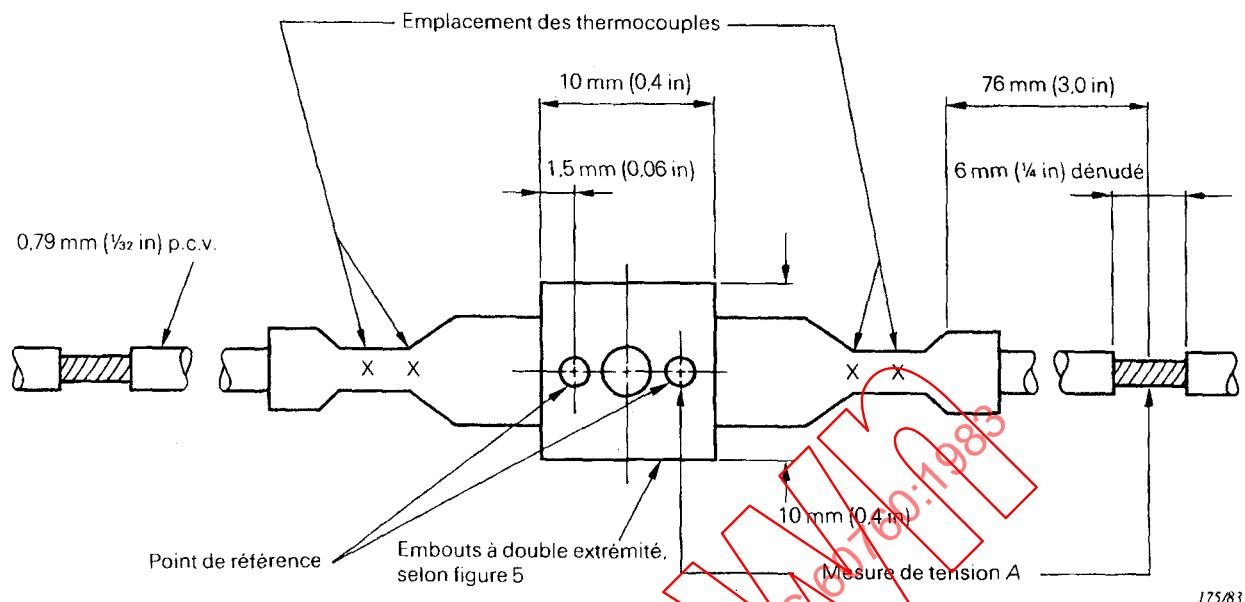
Emplacement des points d'essai et des thermocouples.
